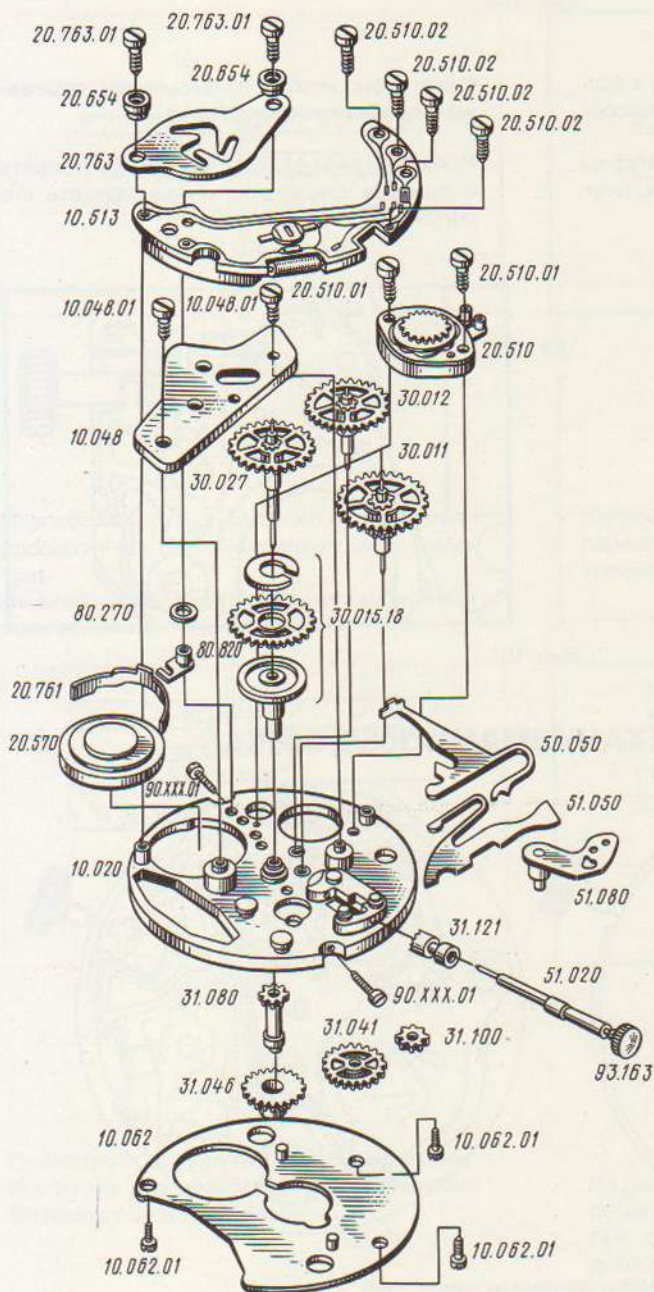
Детали и сборочные единицы механизма часов 3056:
